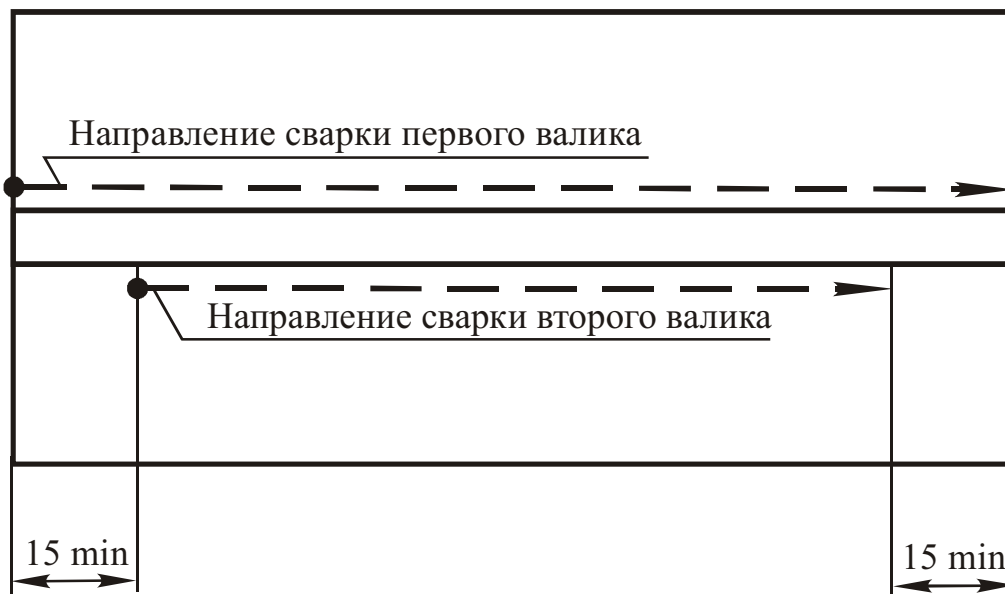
Схема выполнения сварки при определении склонности металла шва к образованию горячих трещин
